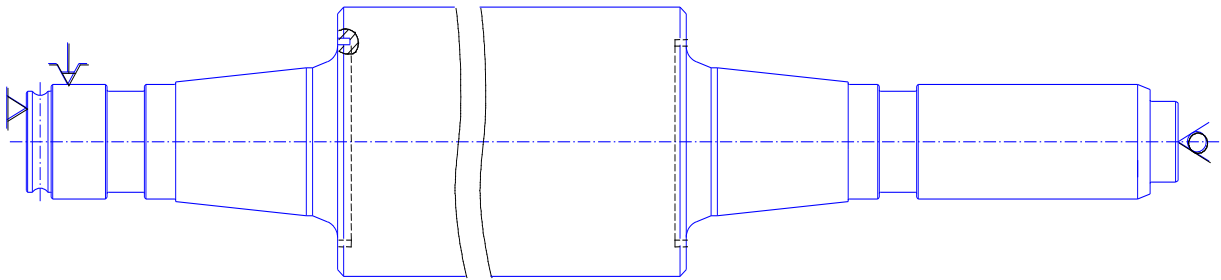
Теоретична схема базування валка на токарних і шліцефрезерній операціях
